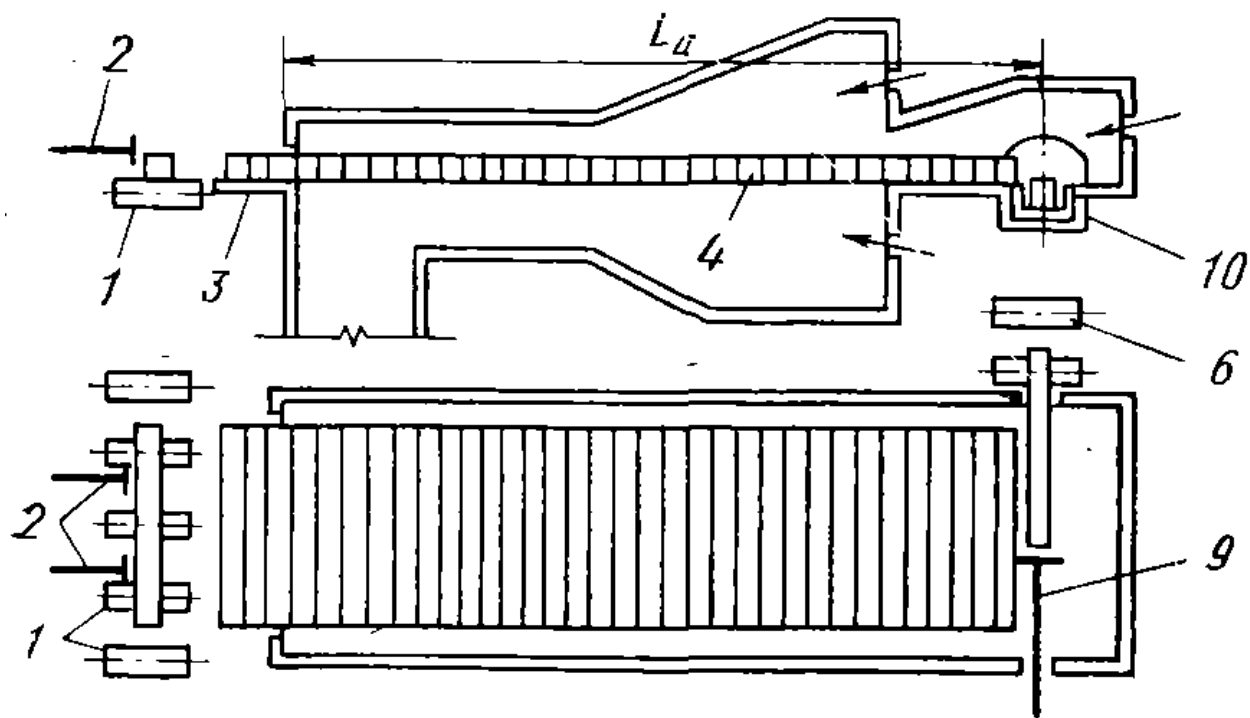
Схема транспортирования заготовок с торцовой загрузкой и боковой выдачей
